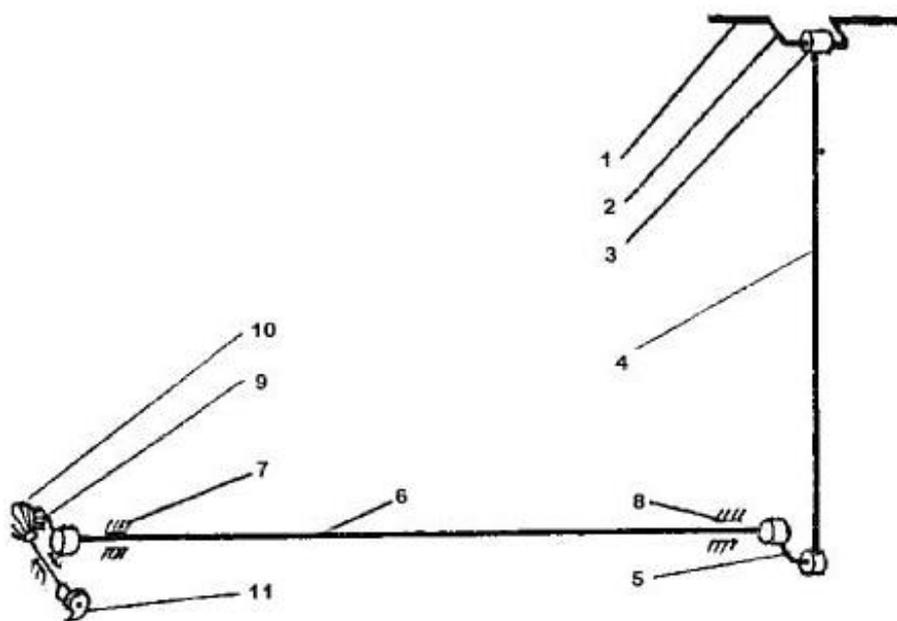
Кинематическая схема механизма челнока машины «Чайка-142М»
